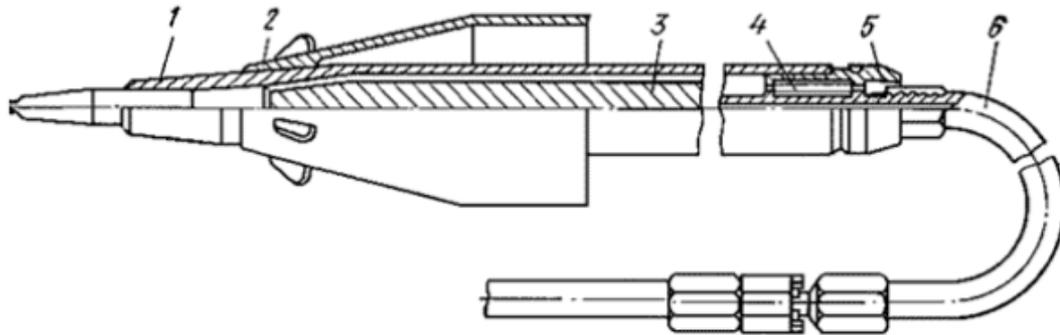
Пневмопробойник: 1 - корпус; 2 - съемный расширитель; 3 - ударник; 4 - золотник; 5 - реверсивное устройство; 6 – рукав.
